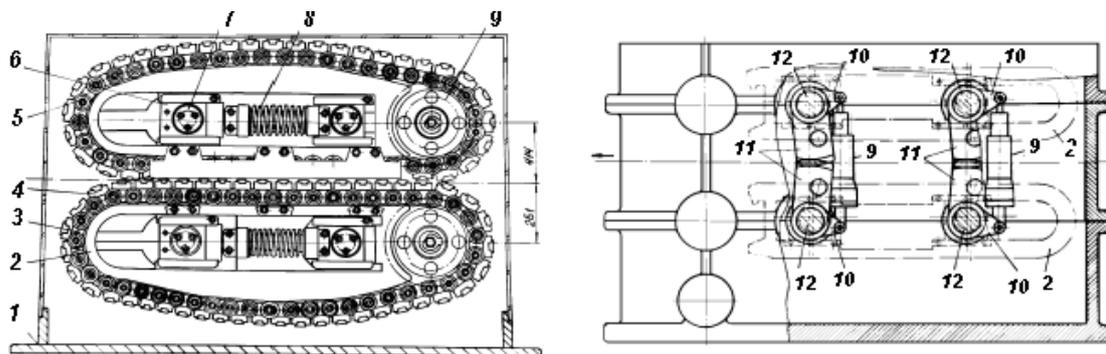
Гусеничный тяговый орган стана для бесконтейнерного циклического прессования прутков из тугоплавких металлов
